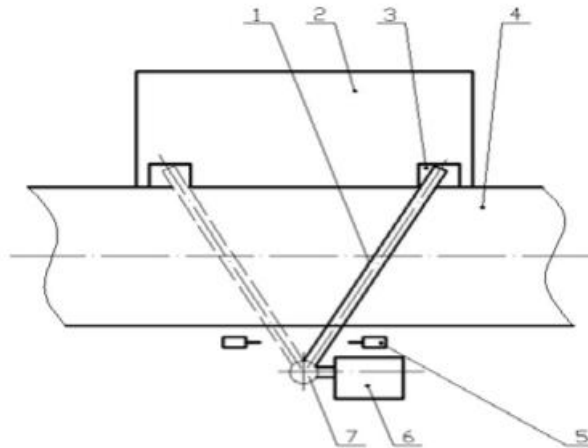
Плуговий скидач: 1 – плуг, 2 – приймальний бункер, 3 – електромагнітний пристрій фіксатору, 4 – конвеєр, 5 – електроперемикач, 6 – двигун-редуктор, 7 – зубчата передача
